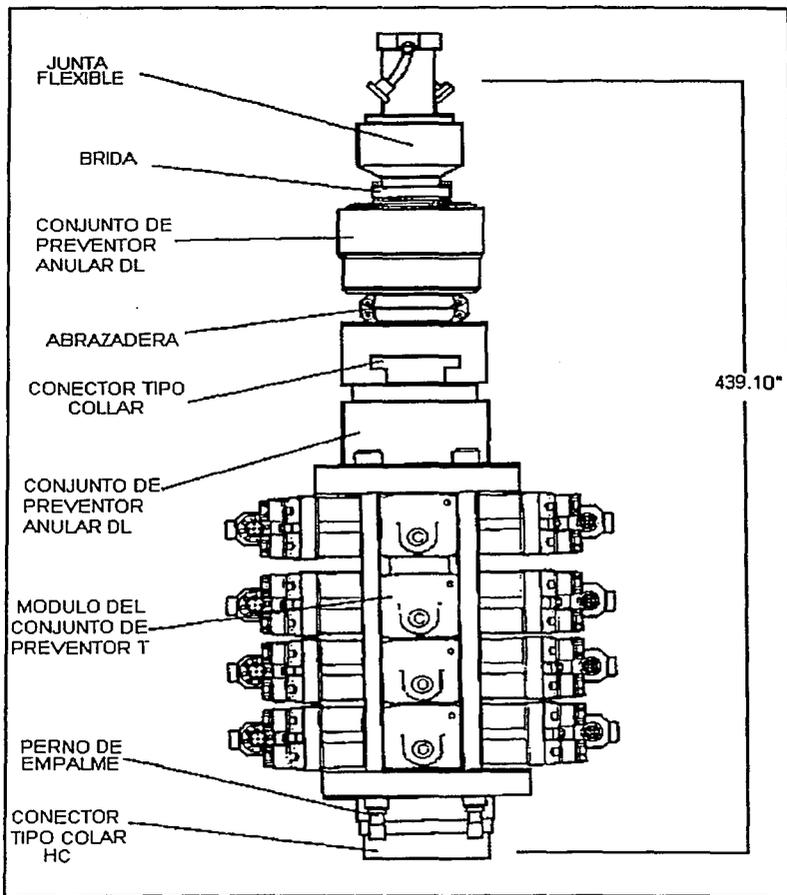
CONJUNTO INFERIOR DEL RISER.⁽⁷⁾
